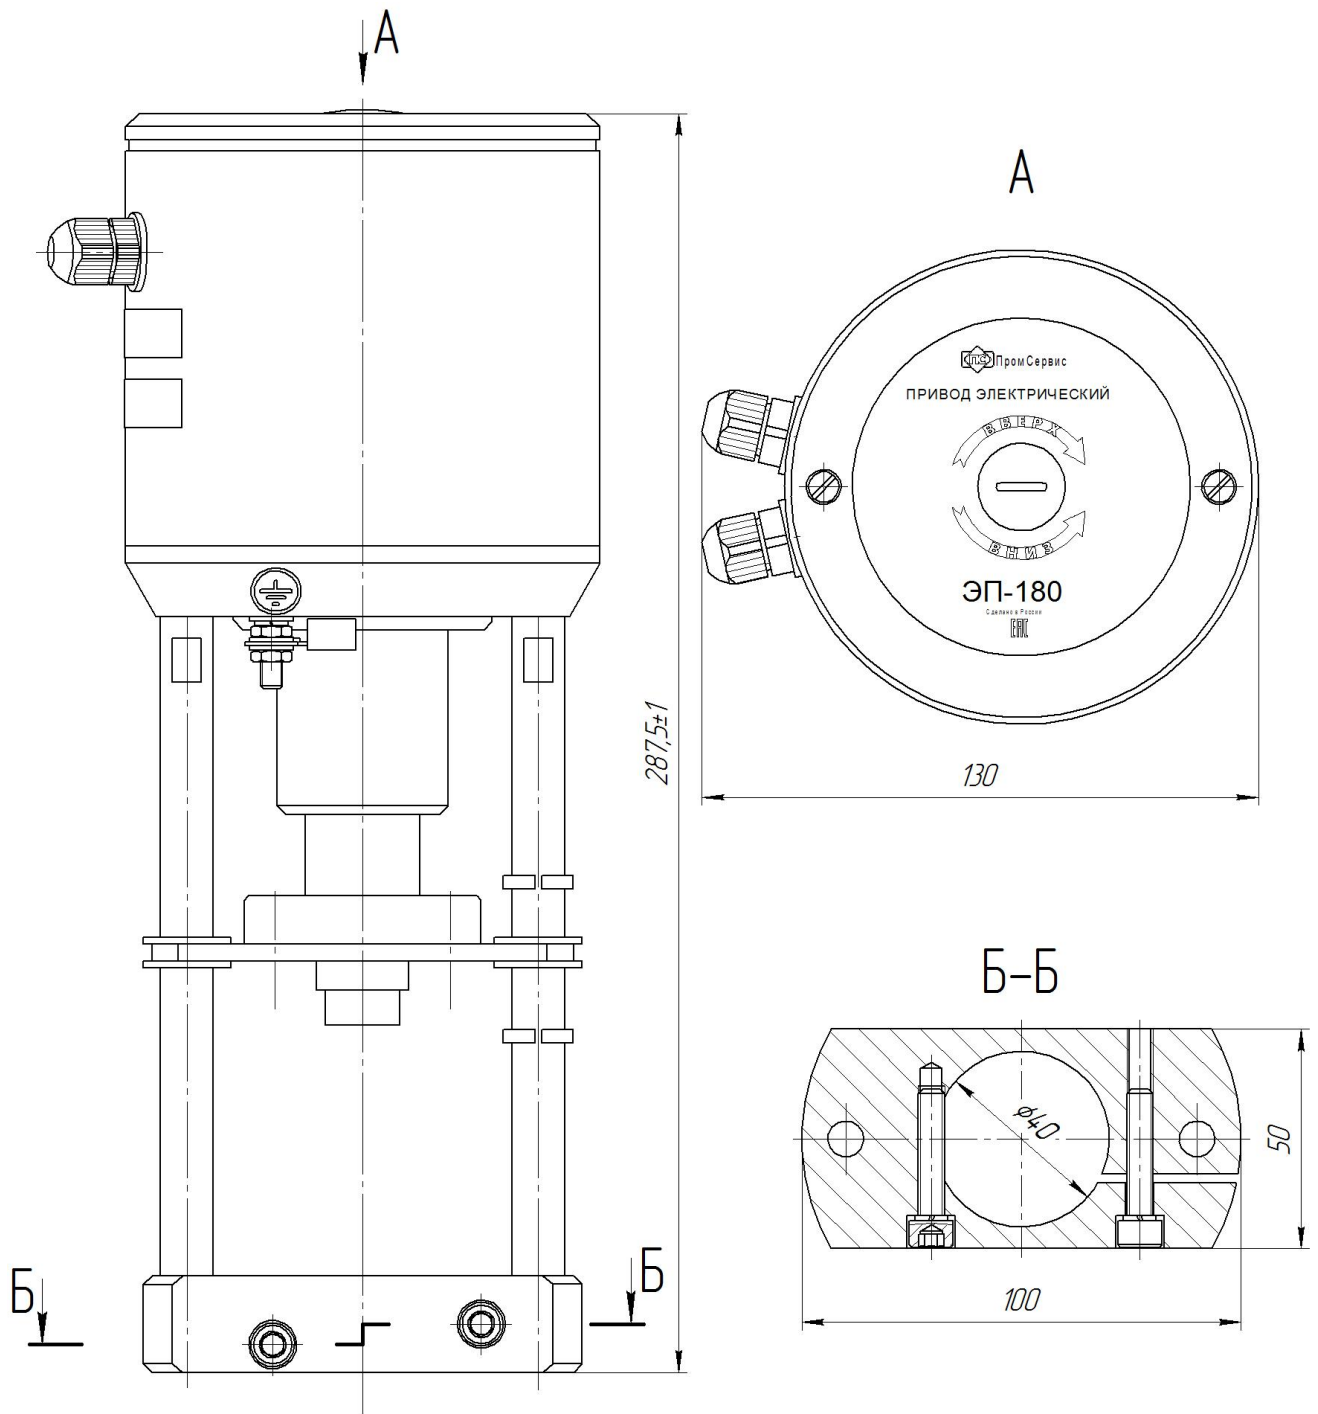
габаритные и присоединительные размеры привода исполнения ЭП-180-01
